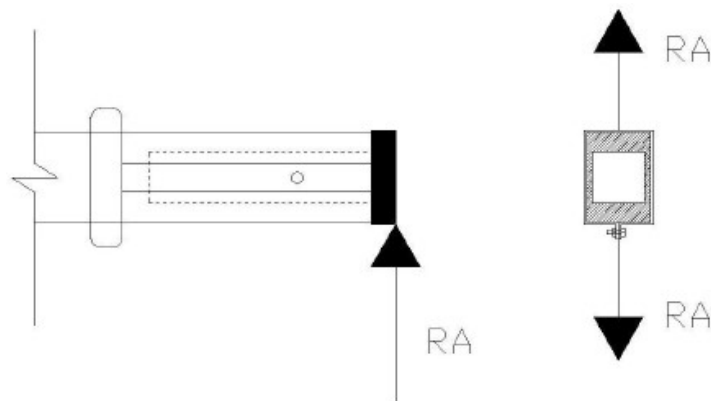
Reforço colocado na ponta da extensão isolante para grua
